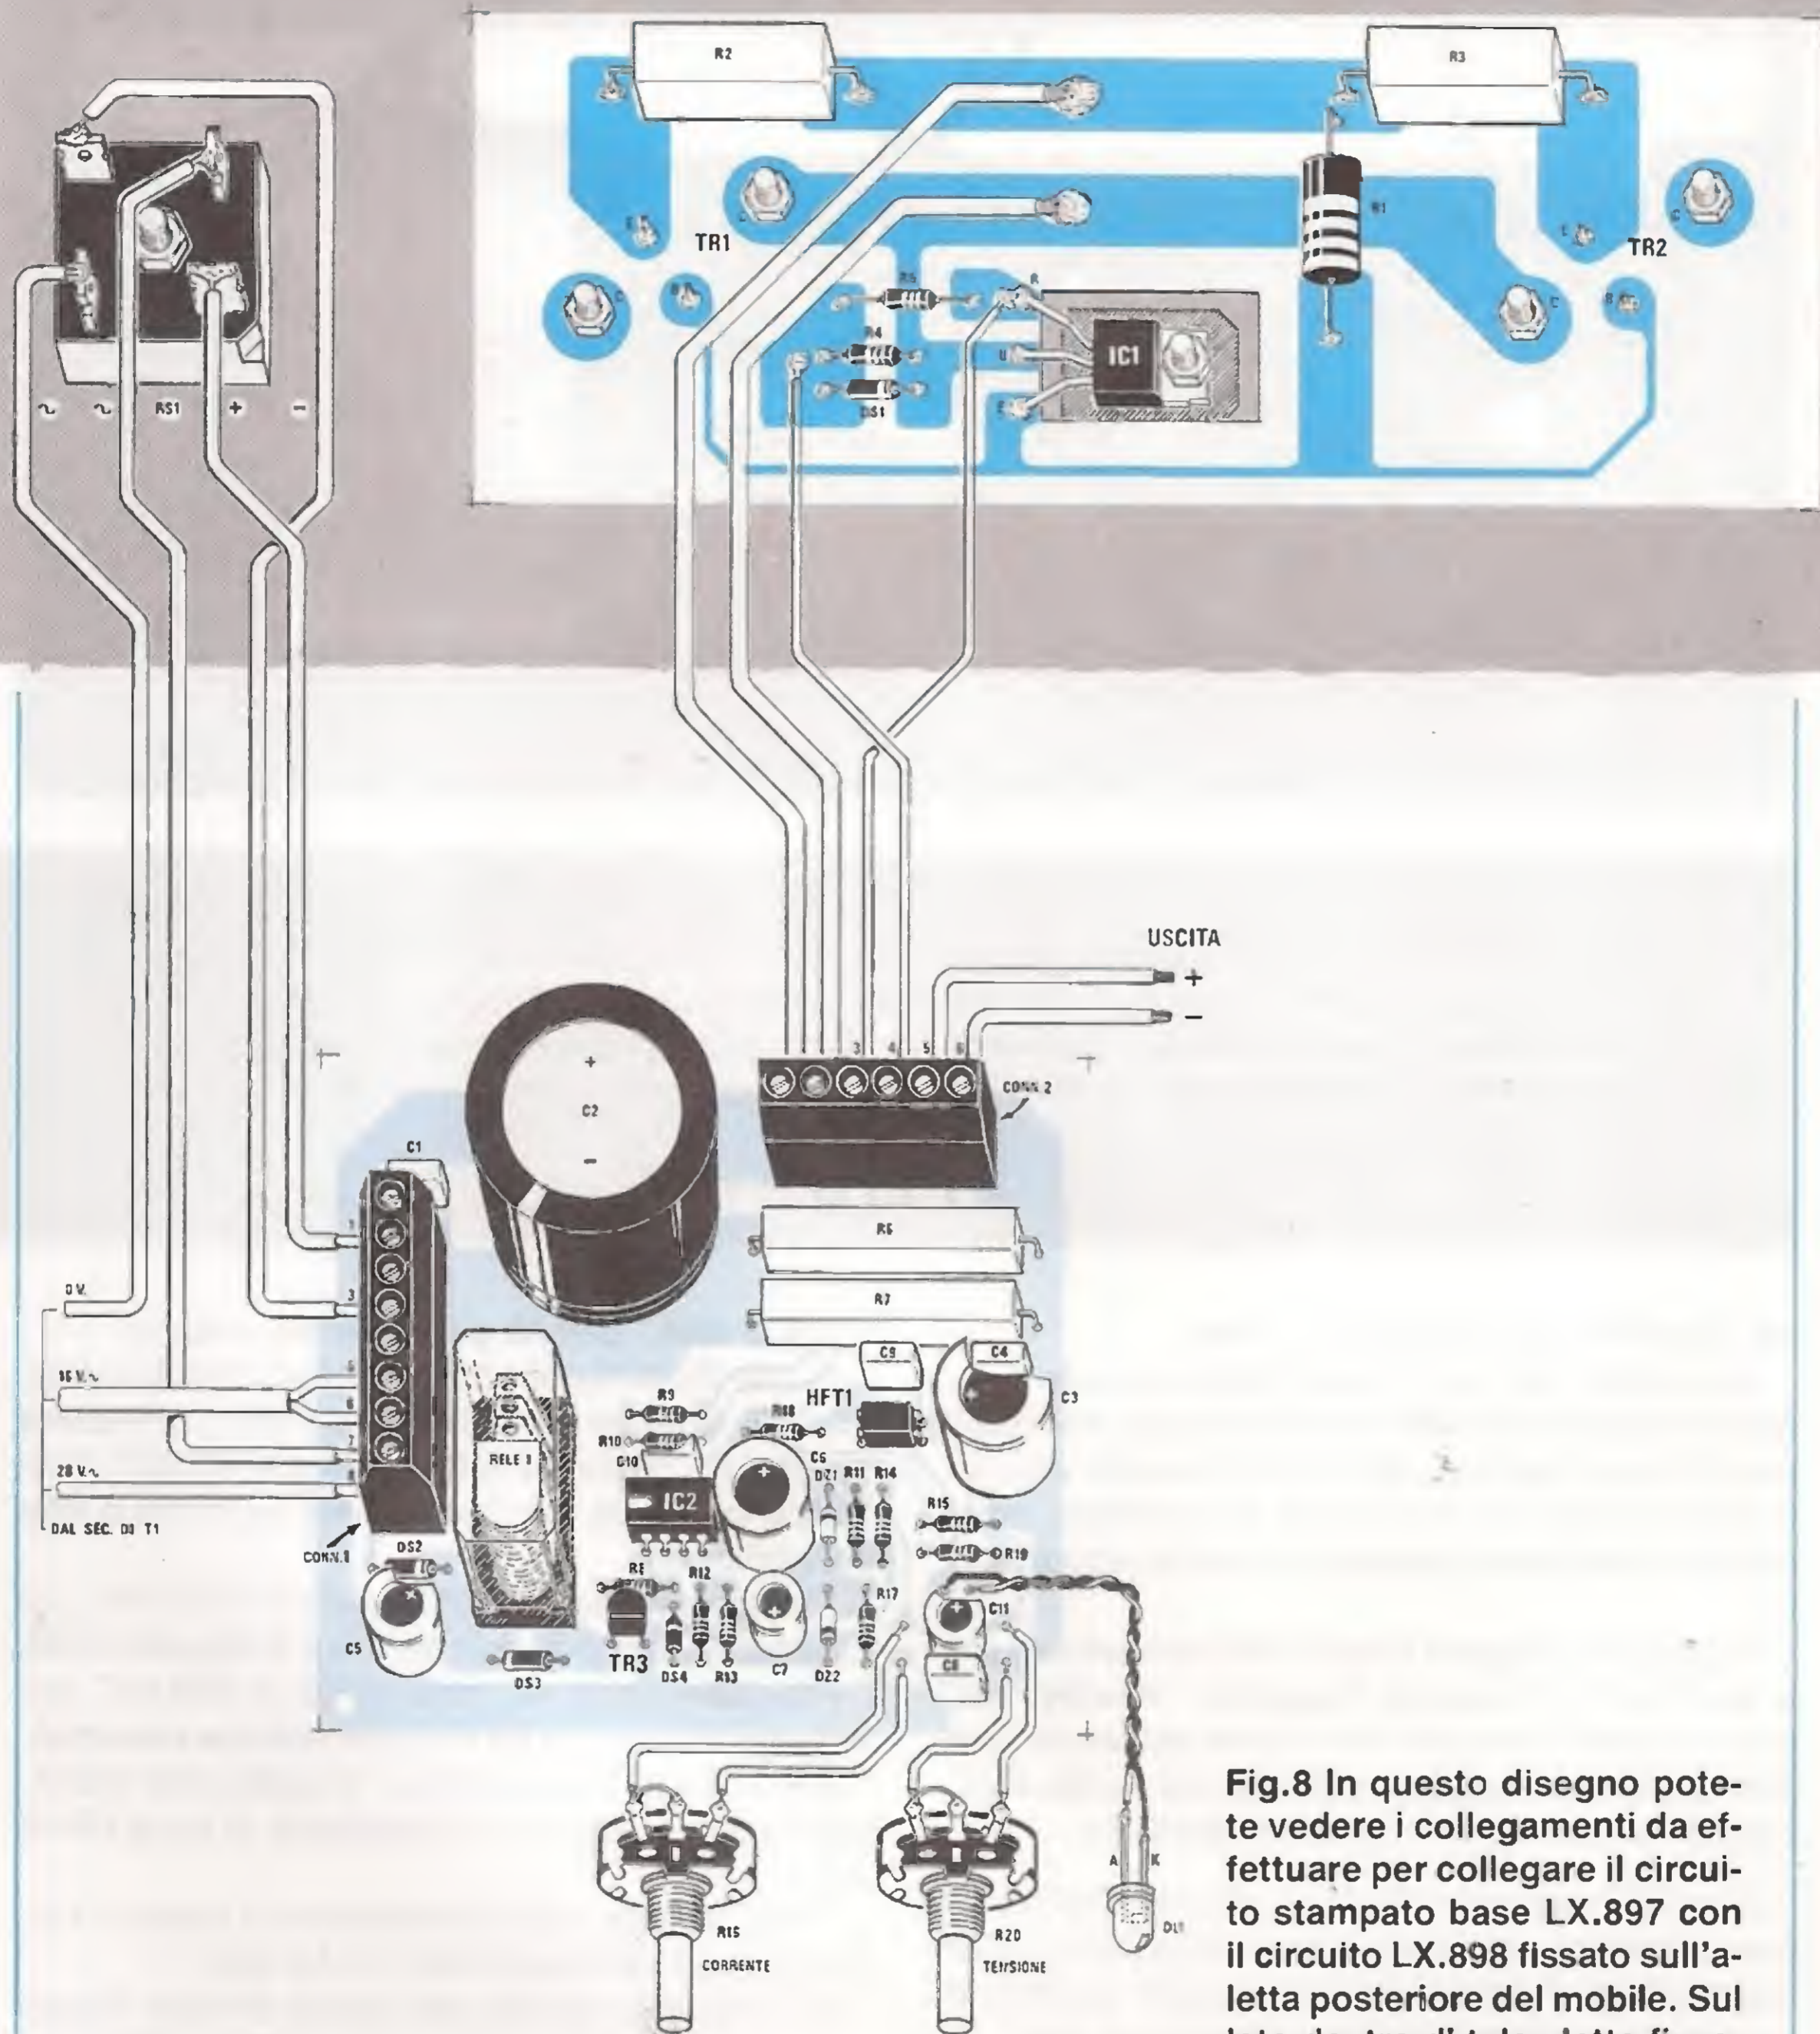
In questo disegno potete vedere i collegamenti da effettuare per collegare il circuito stampato base LX.897 con il circuito LX.898 fissato sull'aletta posteriore del mobile. Sul lato destro di tale aletta fissate anche il ponte raddrizzatore da 25 amper. Si noti la mica posta sotto all'integrato IC1.
